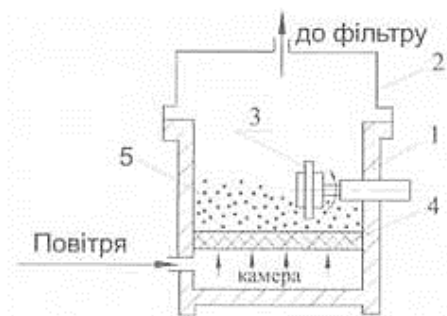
схема турбоабразивної обробки: 1 – корпус установки; 2 – кришка; 3 – оброблювана деталь; 4 – розподільна решітка; 5 – кипячий шар абразивних зерен.
